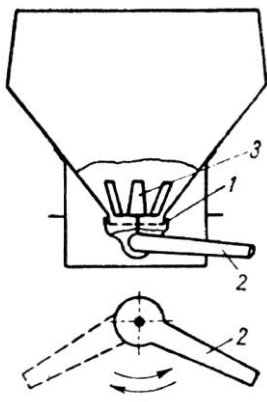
Mașină de împrăștiat îngrășămintele cu aparat de împrăștiere cu tub tronconic:
